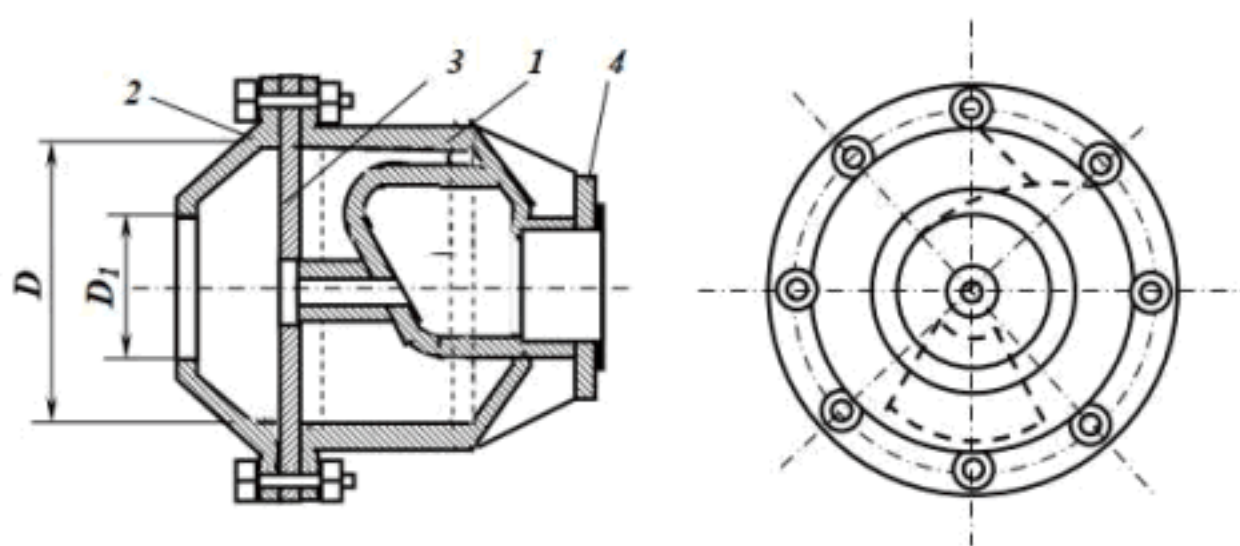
Барабанний живильник: 1 – корпус; 2 – кришка; 3 – діафрагма; 4 – фланець [3]
